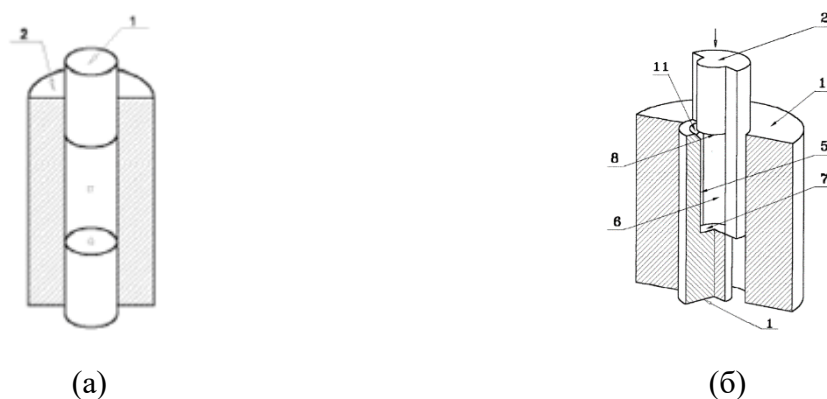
Цилиндрические формы для сухого прессования: (а) – стандартная форма (1 - пуансон, 2 - матрица); (б) – форма для коллекторного прессования: 1, 2 – формообразующие элементы; 5, 6 – части пассивной формообразующей поверхности первого и второго элементов пресс-формы; 7, 8 – часть активной формообразующей поверхности первого и второго элемента пресс-формы; 10 – конструктивный элемент, удерживающий элементы 1 и 2 от неосевых перемещений; 11 – технологическая проточка на элементе пресс-формы для облегчения загрузки порошка [56]
